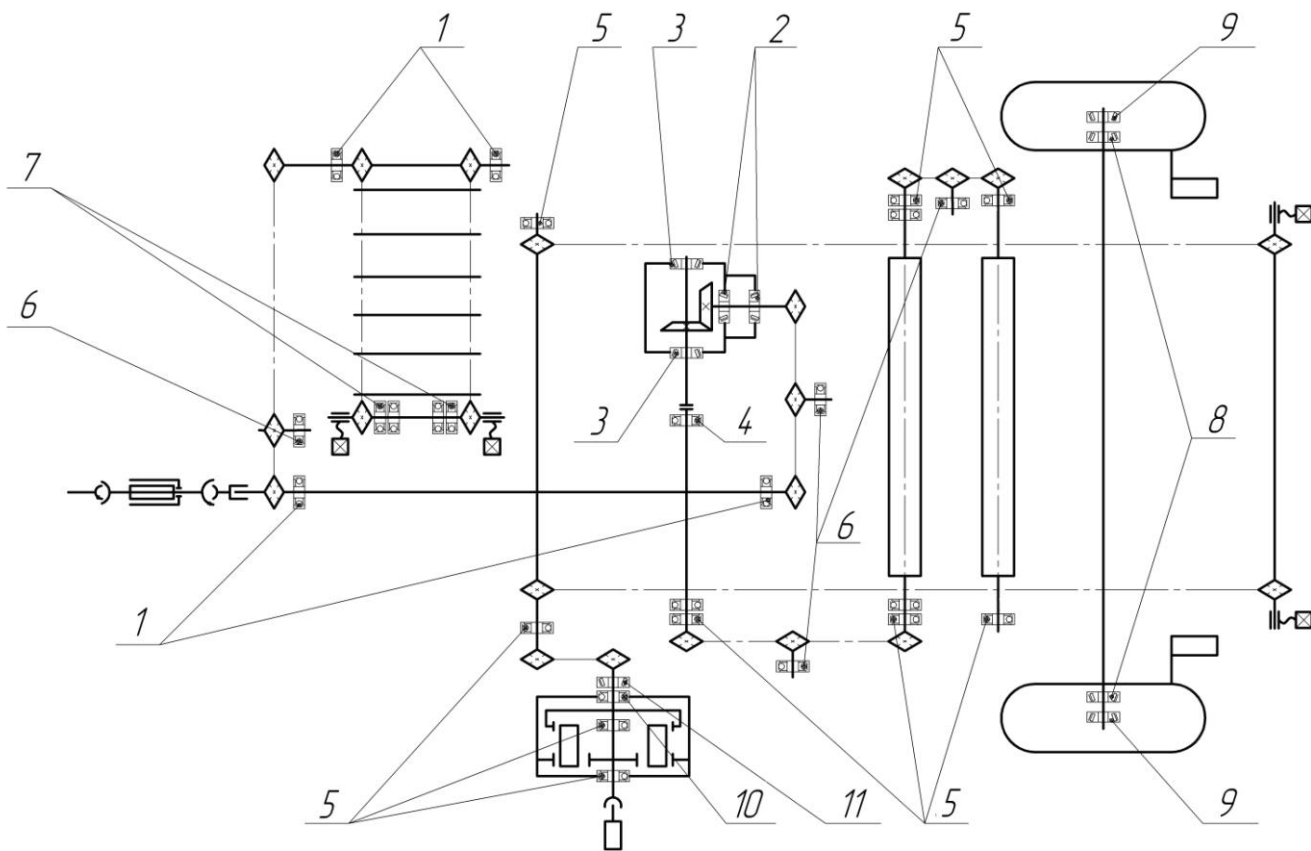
Схема расположения подшипников КР-Ф-10
